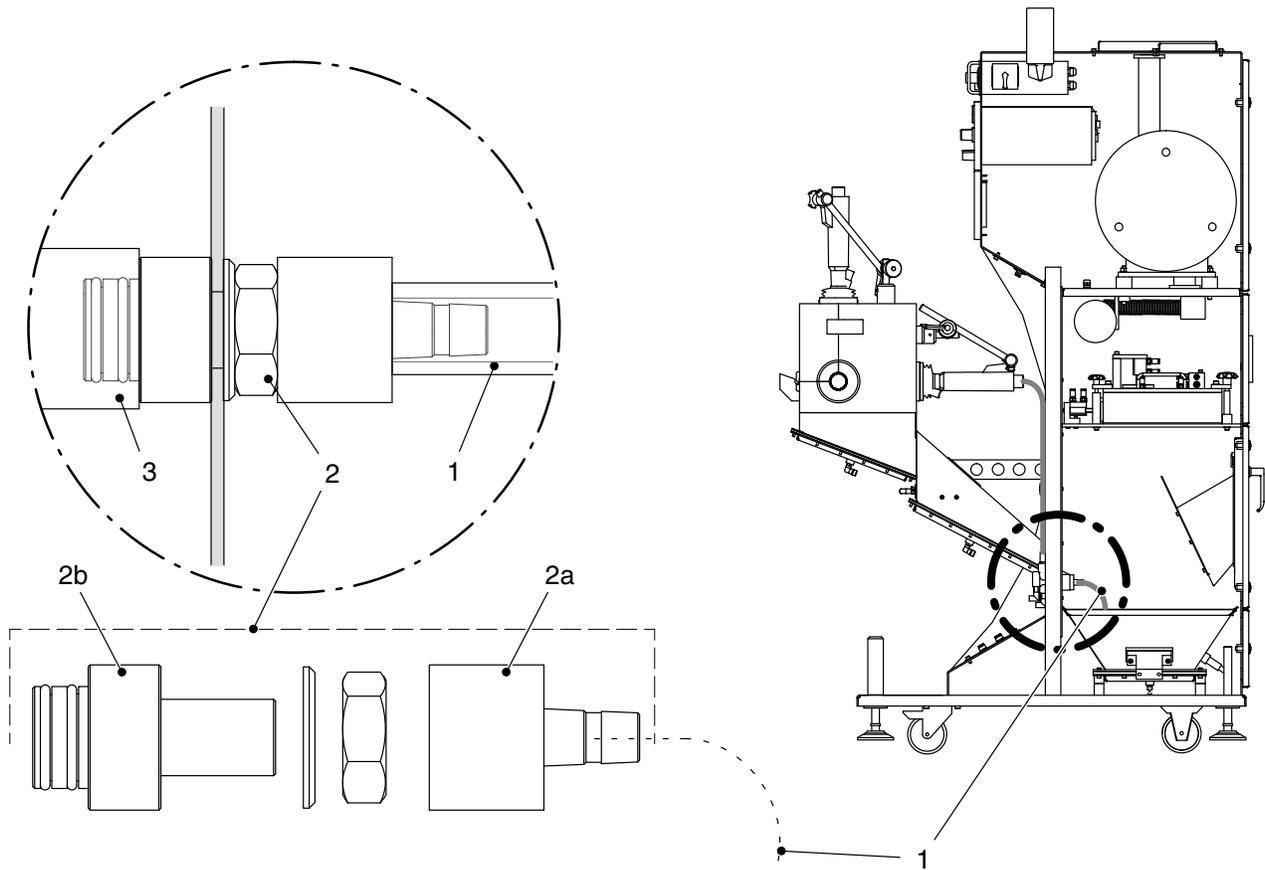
Montage de l'adaptateur de pompe en aluminium
